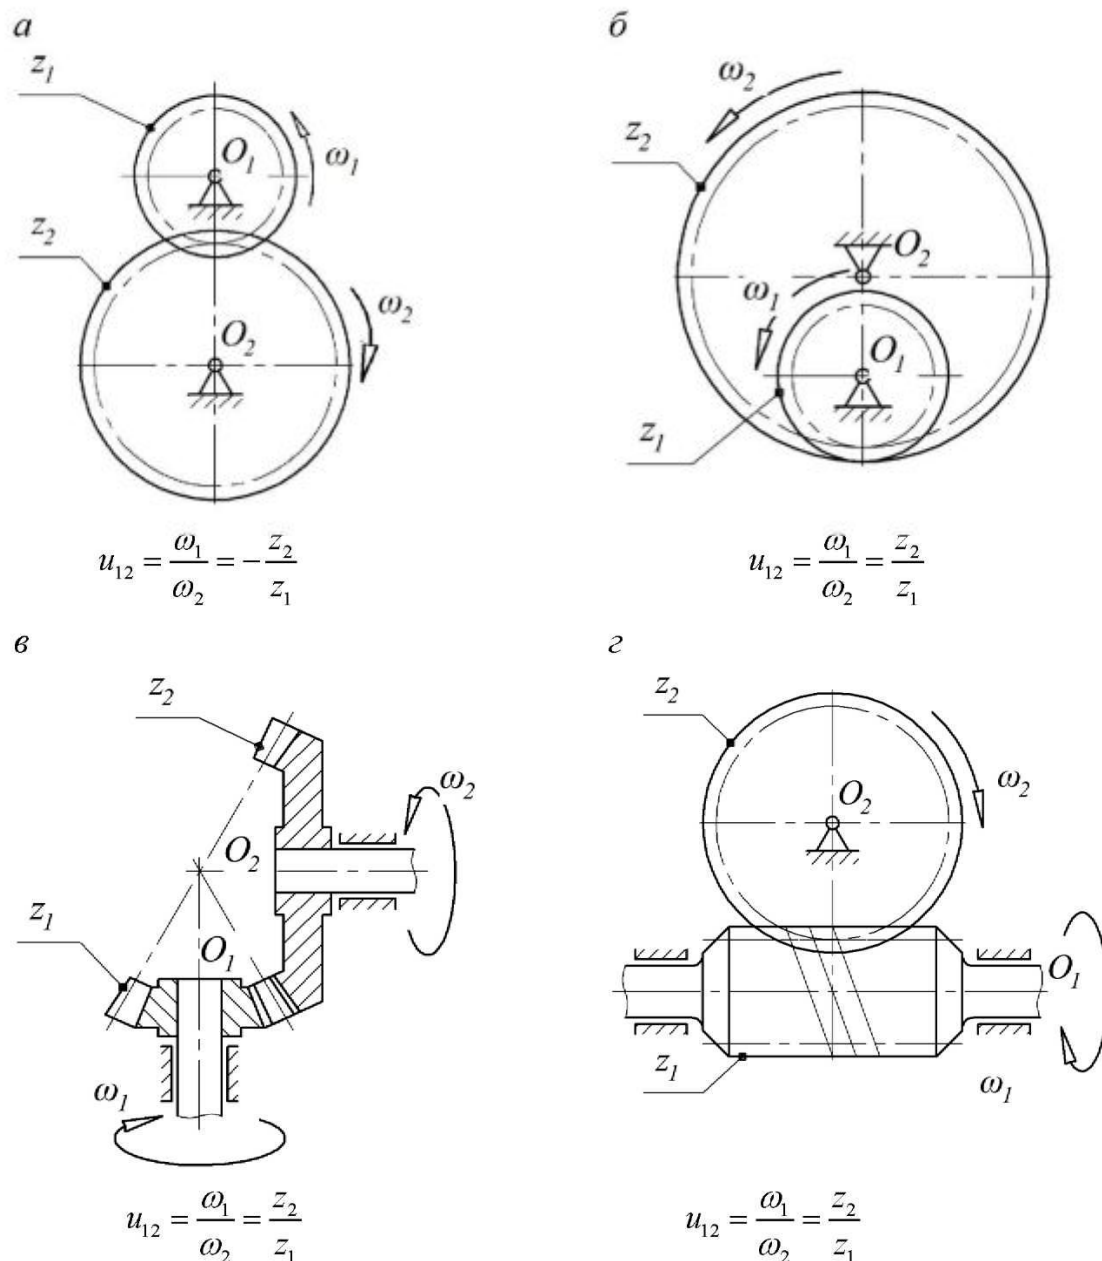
Простые (одноступенчатые) механизмы с неподвижными осями колес: а – внешнее зацепление; б – внутреннее зацепление; в – передача с коническими колесами; г – червячная передача
